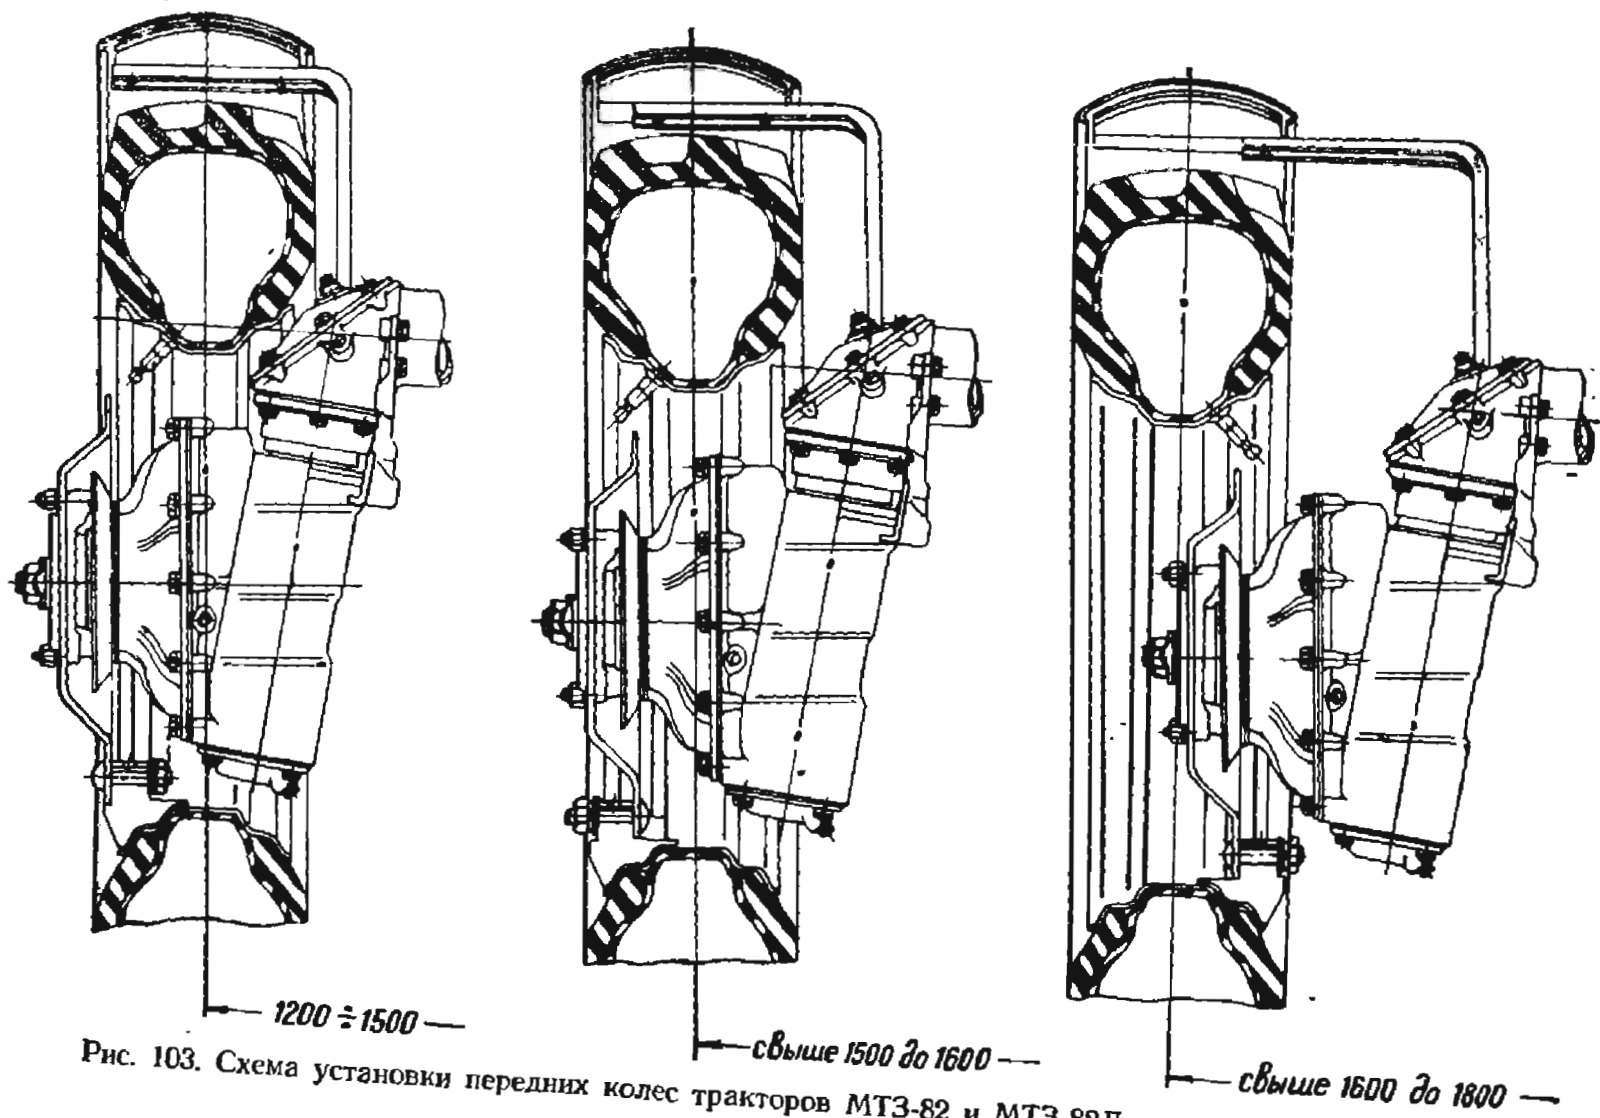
Схема установки передних колес тракторов МТЗ-82 и МТЗ-82Л на различную колею.
